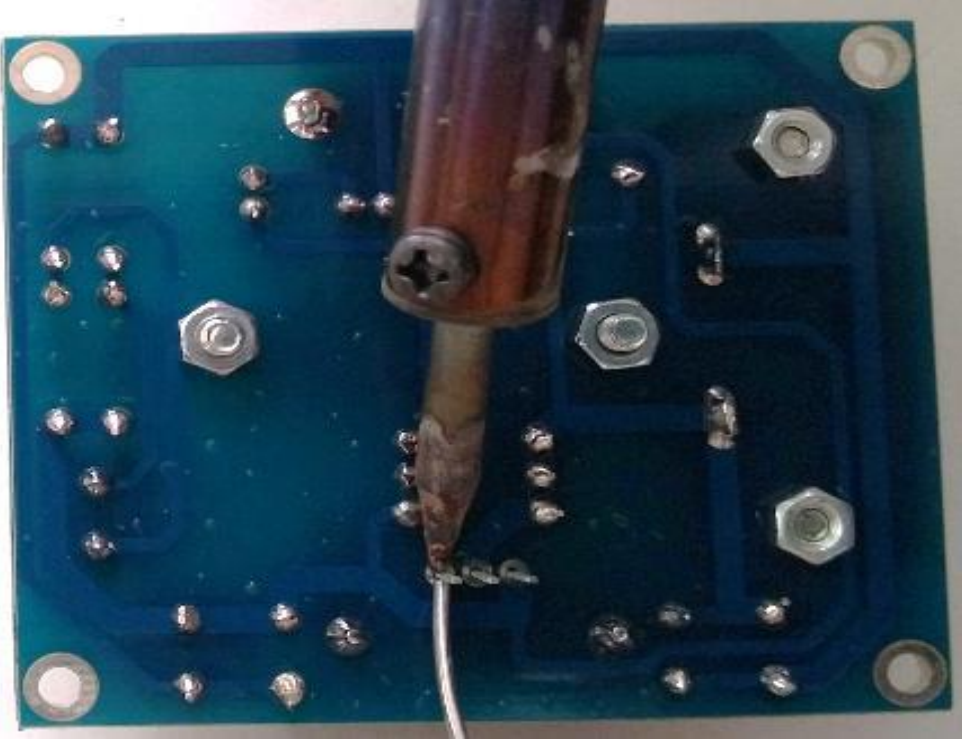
Güç kaynağı-2 LM317 entegre ve soğutucunun montajı
